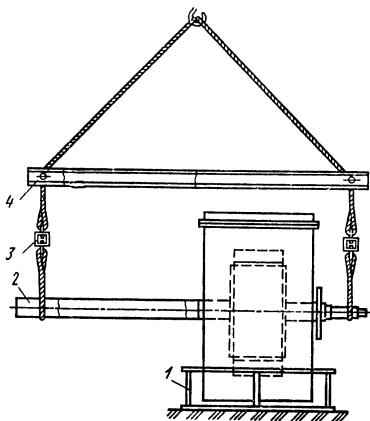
Приспособление для вывода ротора электродвигателей типа ДАЗО 15-го и 19-го габаритов
